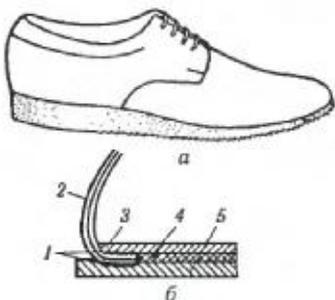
Клеюве кріплення: а — загальний вигляд взуття; б — схема кріплення; 1 — клейові плівки; 2 — заготовка; 3 — устілка; 4 — прокладка; 5 — підошва
